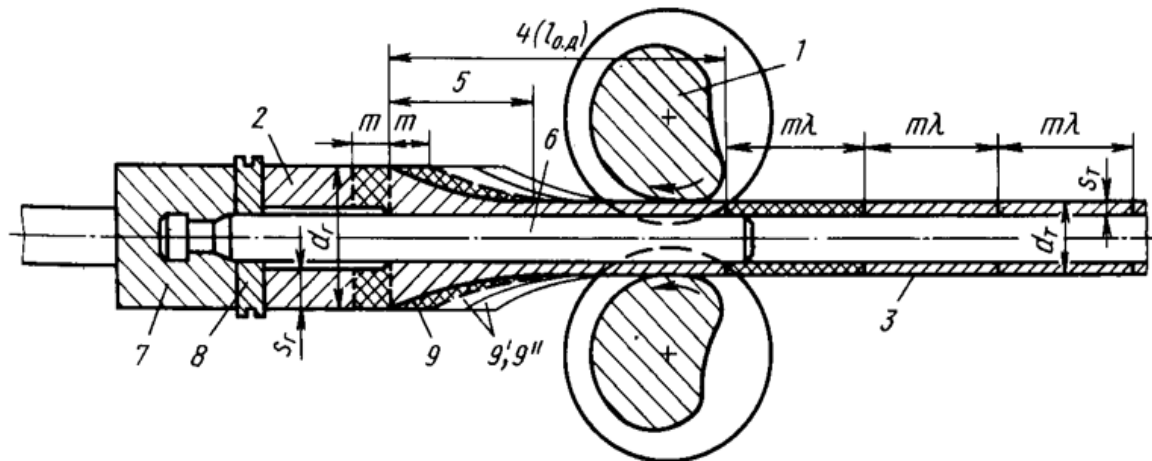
Схема прокатки в пилигримовом стане: 1 – валок; 2 – гильза; 3 – труба; 4 – очаг деформации (рабочий конус); 5 – пильгерголовка; 6 – оправка (дорн); 7 – замок оправки и шток подающего аппарата; 8 – кольцо для упора гильзы при прокатке и удержания ее при извлечении оправки; 9, 9', 9'' – смещенный объем металла, в данном цикле (равный объему подачи)
